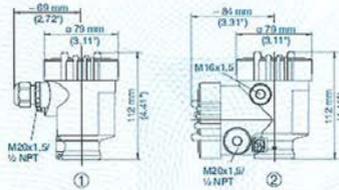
Пластиковий корпус (1 – однокамерний; 2 - двокамерний)
